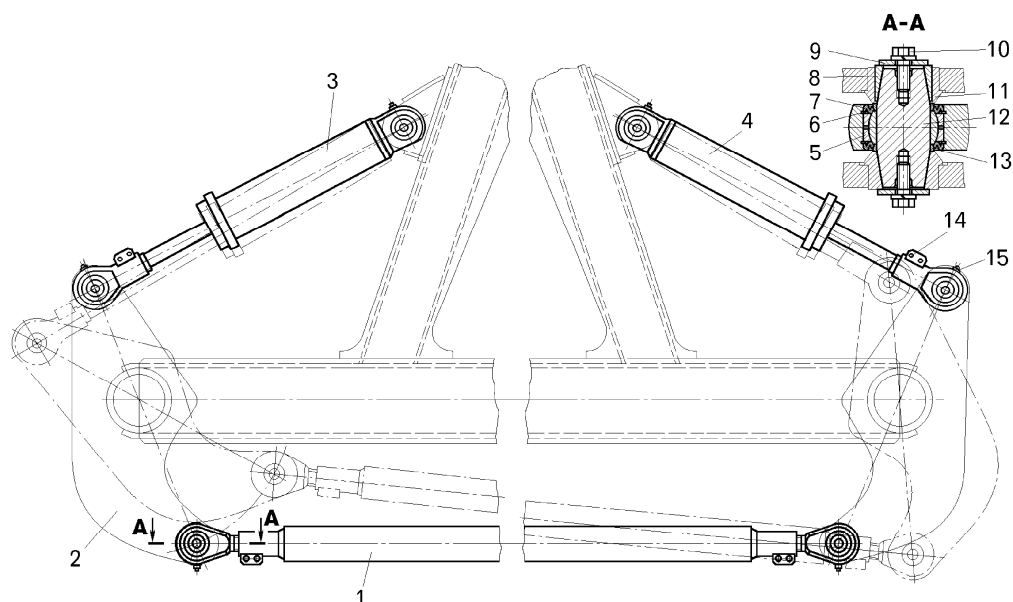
Установка рулевой тяги и гидроцилиндров поворота:
